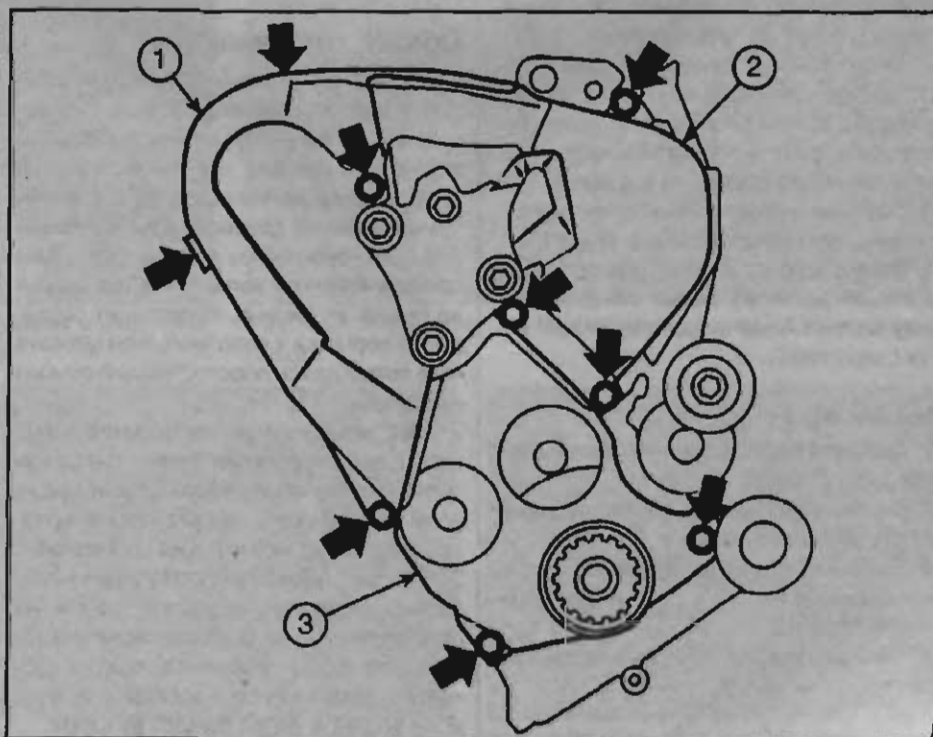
Расположение болтов крепления кожухов зубчатого ремня: 1 – верхний кожух; 2 – промежуточный кожух; 3 – нижний кожух
